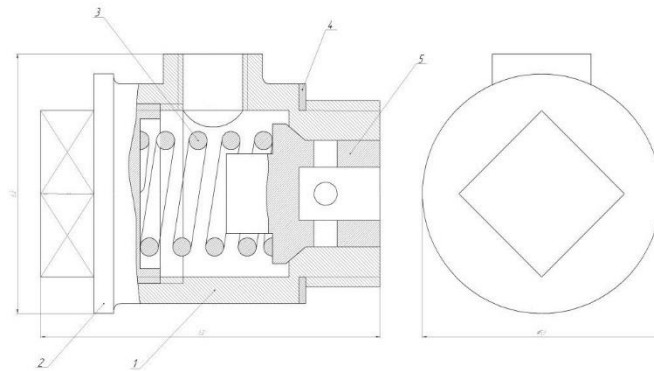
Запобіжний клапан: 1 – корпус; 2 – кришка; 3 – пружина; 4 – шайба; 5 – поршень.
